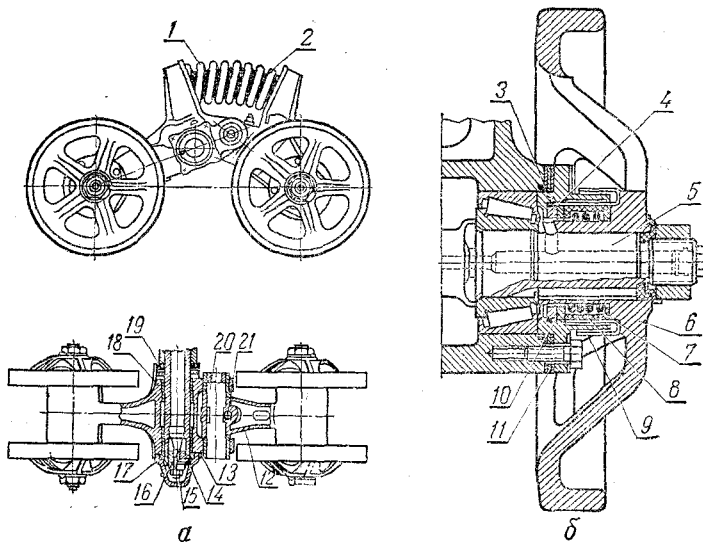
Балансирная каретка подвески тракторов Д-75 и ДТ-75М:
